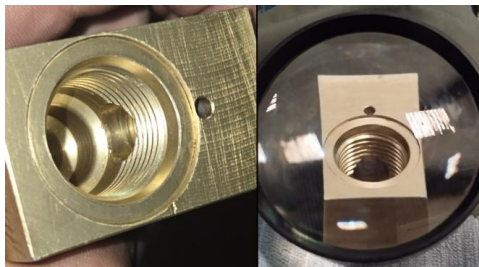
Desmontaje y desconexión de los bloques manifold
